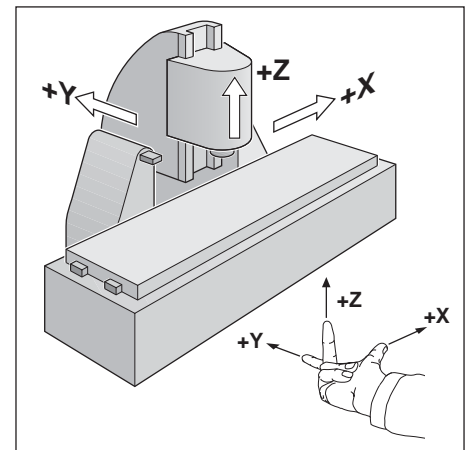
Désignation et sens des axes de la machine sur une fraiseuse
